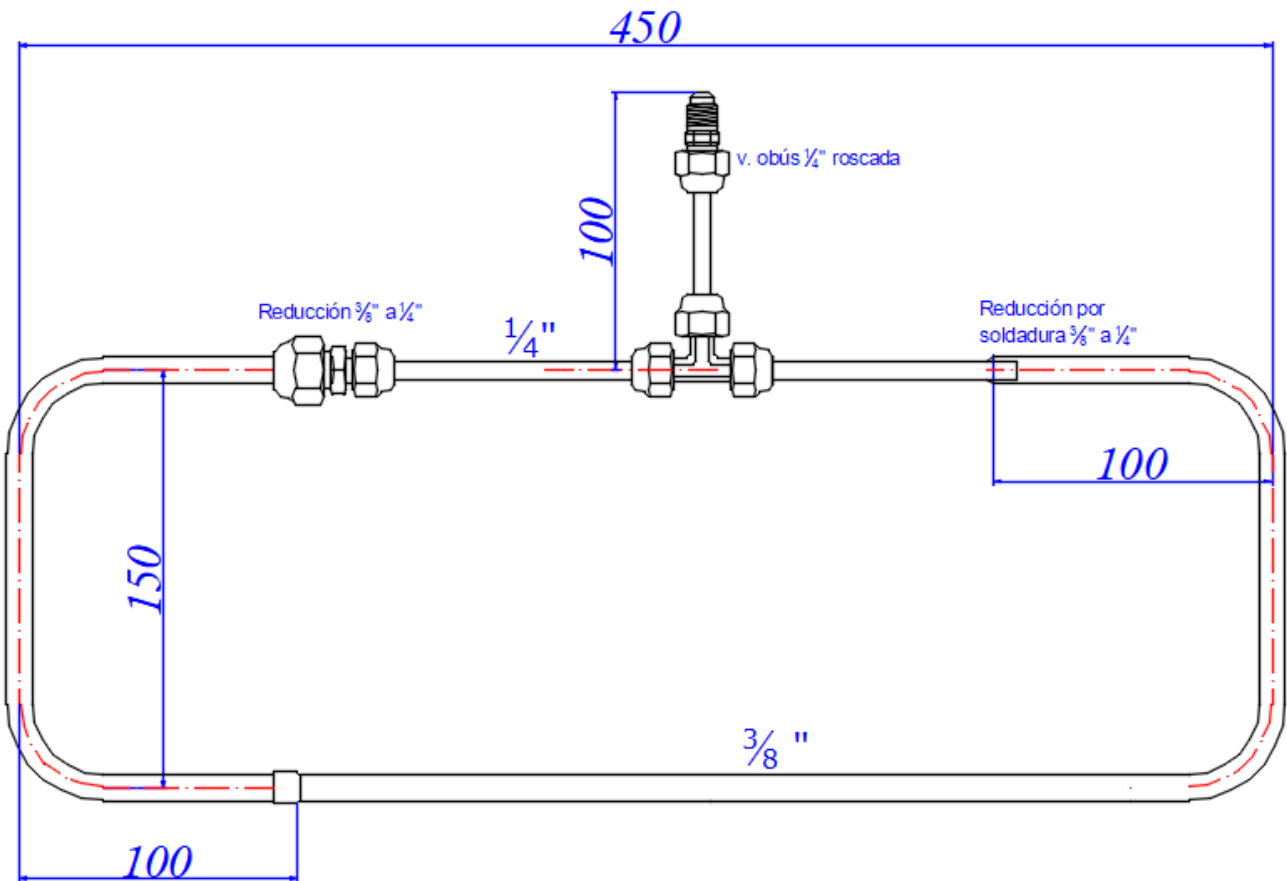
Mecanitzat amb tub de coure amb accessoris i soldadura.
